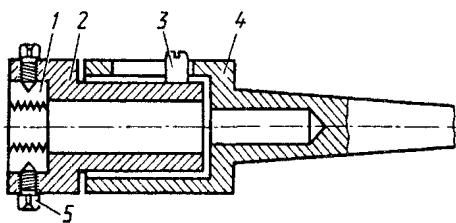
Самовисувний хитний плашкотримач: 1 - плашка; 2 - плашкотримач; 3 - штифт; 4 - корпус; 5 - гвинт
